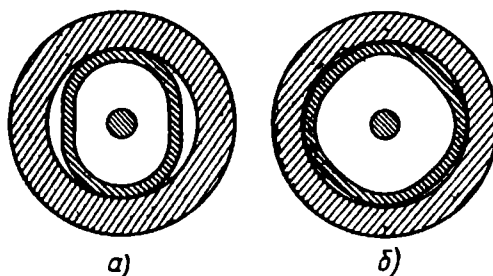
Схемы двигателей с гибкими волновыми роторами
